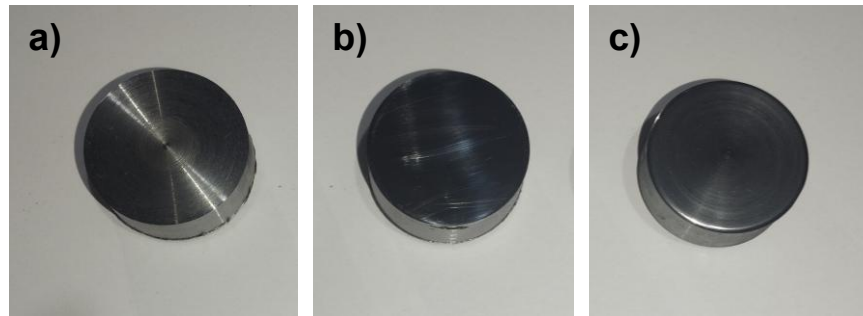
Surfaces planes préparées : a) usiné ; b) usiné puis poli ; c) usiné puis bruni
